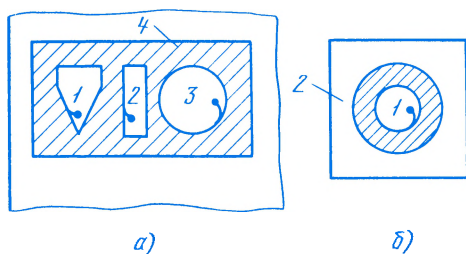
Приемы резки внутри контура изделия: а — начало резки, б — вырезка фланцев; 1, 2, 3, 4 — последовательность резов
